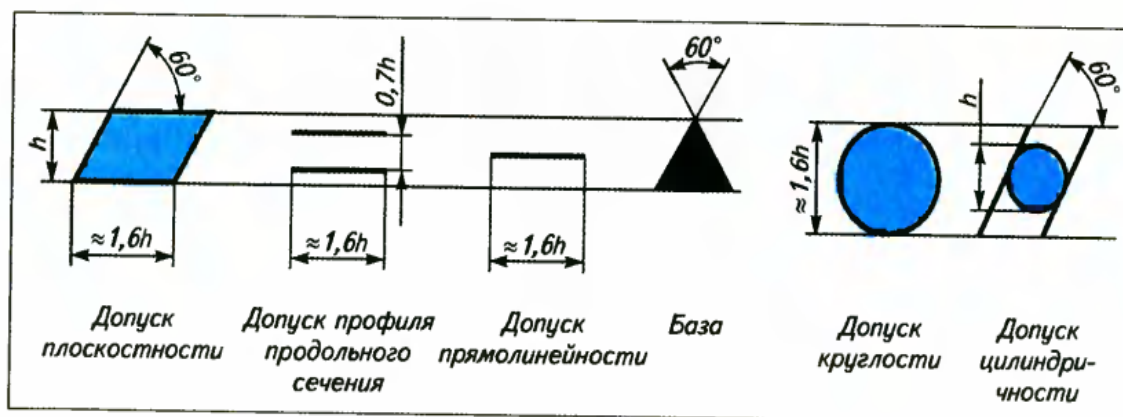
Формы и размеры знаков для условных обозначений видов допусков формы
